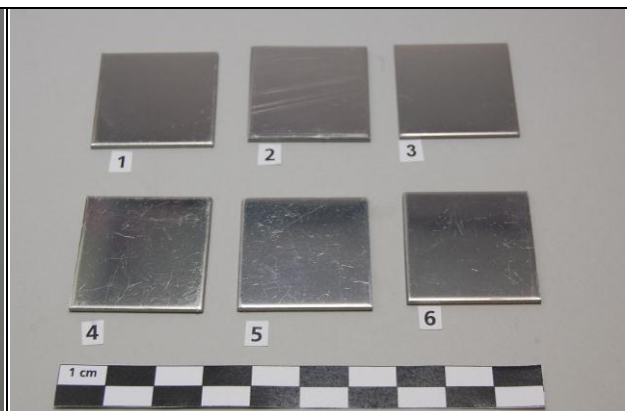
Stahlplättchen mit Halogenstrahler GU 10 beleuchtet
